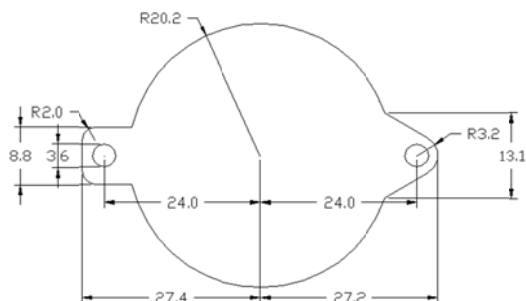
Соединительный фланец передатчика - тип JUNIOR
